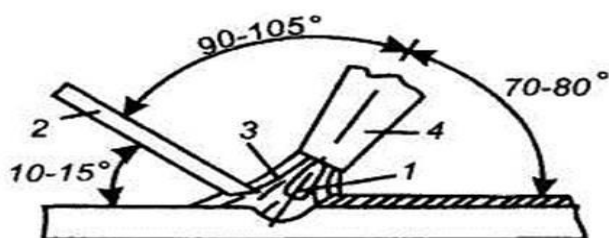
Расположение горелки и присадочного прутка при ручной аргонодуговой сварке: 1 – электрод; 2 – присадочный пруток; 3 – защитный газ; 4 – сопло
